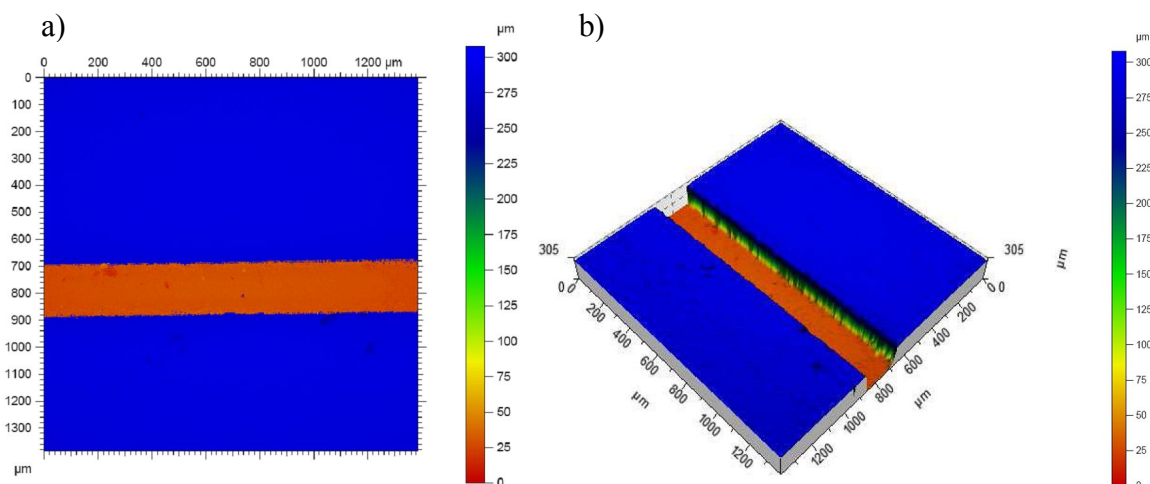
Geometrické měření mikrozasobníku v místě řezu B
